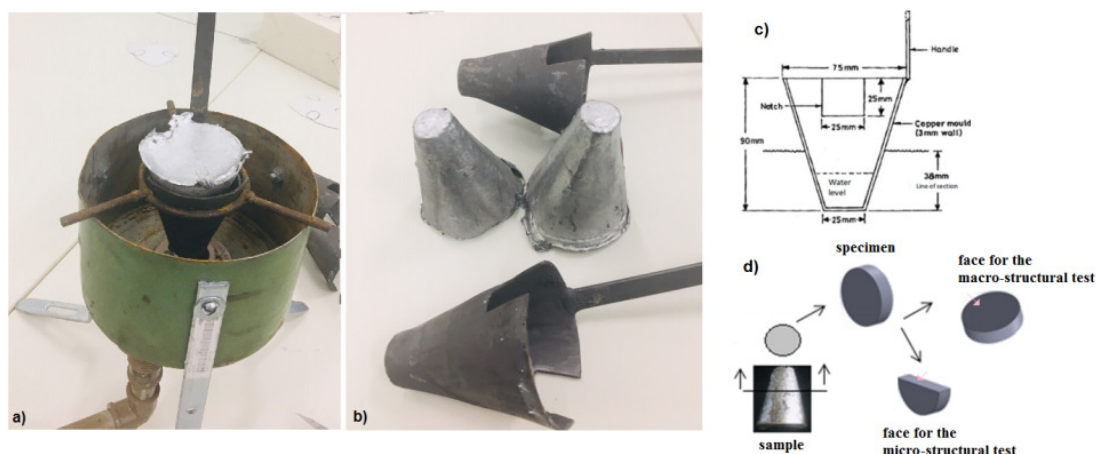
Teste TP1-2012. a) Conjunto montado para resfriamento. b) Painel do molde e amostras. c) Dimensões do molde. d) Corte da amostra.
